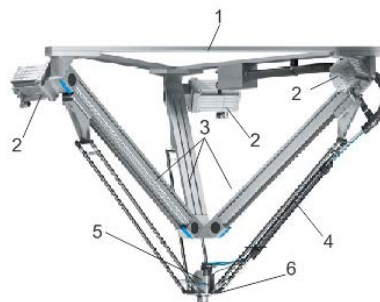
Электромеханические конструкции робота-трипода: 1- неподвижная платформа; 2- сервомоторы; 3- каретка механических преобразователей; 4- тяги; 5- поворотный серводвигатель; 6- подвижная платформа.
